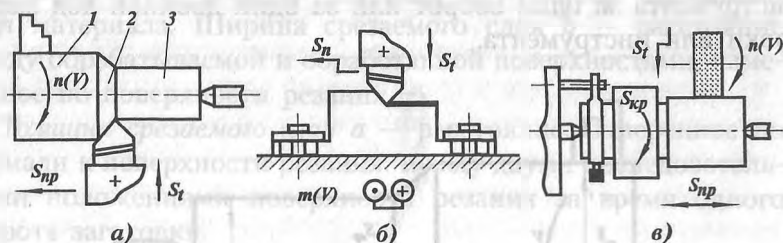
Схемы обработки заготовок: точением (а), строганием (б), шлифованием (в):  $S_{пр}$  — продольная подача;  $S_{п}$  — поперечная подача;  $S_t$  — установочное движение
